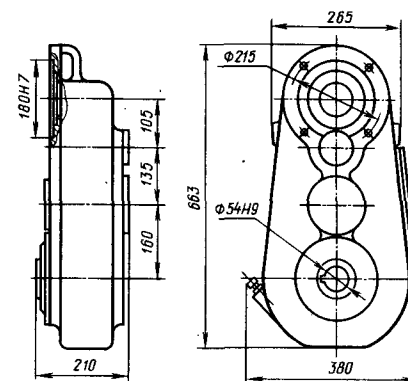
Габаритные и присоединительные размеры редуктора А-400
